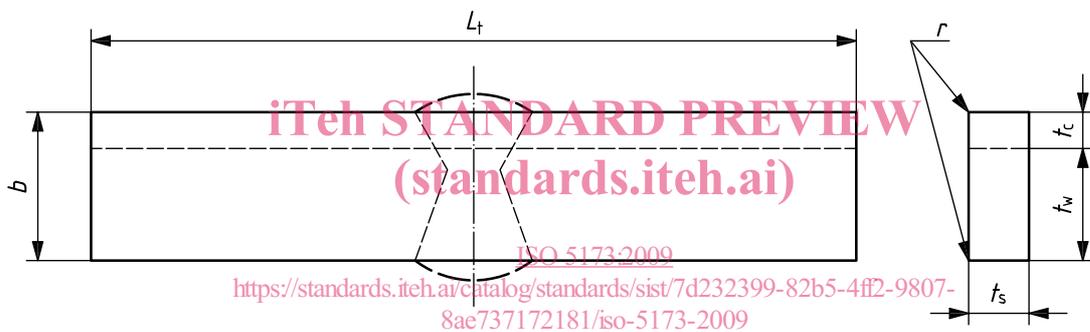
Éprouvette de pliage de côté sur revêtement sur soudure bout à bout (SBCB)
